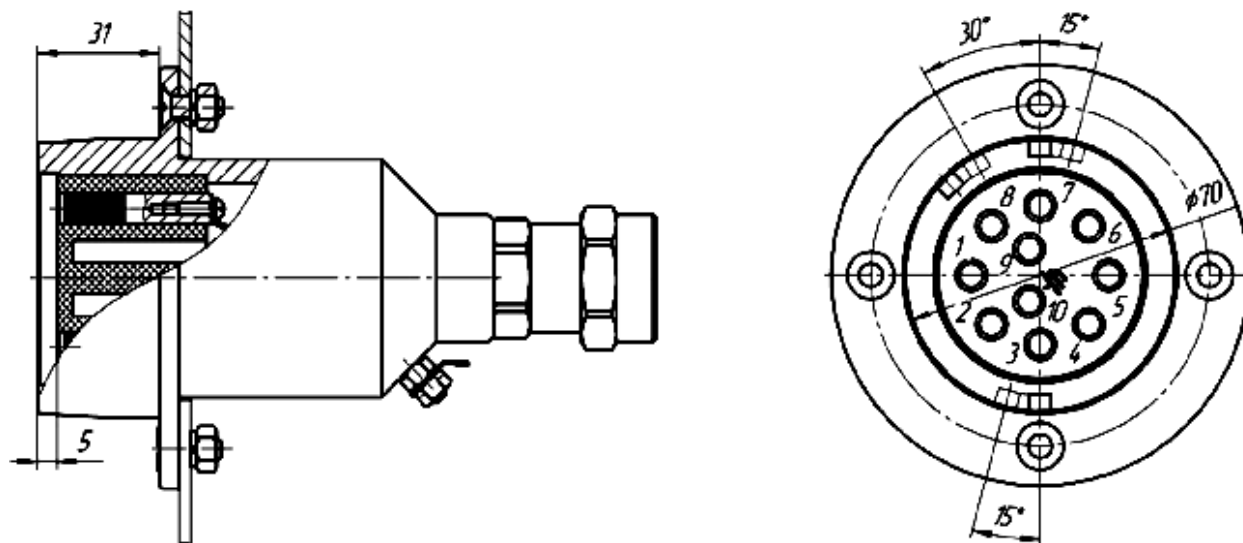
Габаритные размеры и расположение контактов розетки соединительной.
